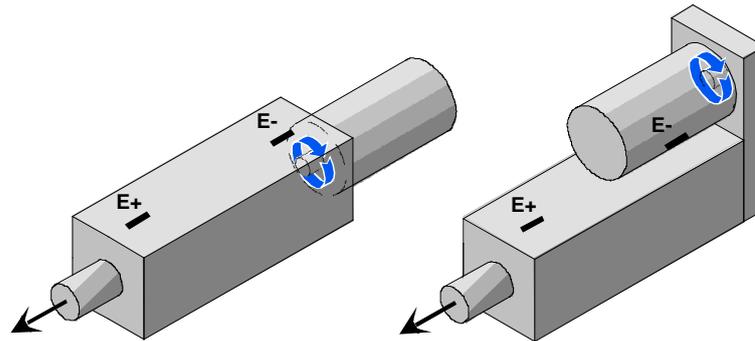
Drehrichtung des Motors beim Ausfahren des Zylinders
